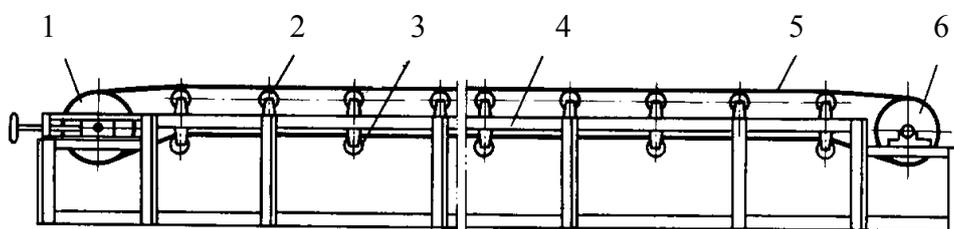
Ленточный конвейер: 1 – натяжной барабан; 2 – опорный ролик; 3 – поддерживающий ролик; 4 – станция; 5 – лента; 6 – приводной барабан
